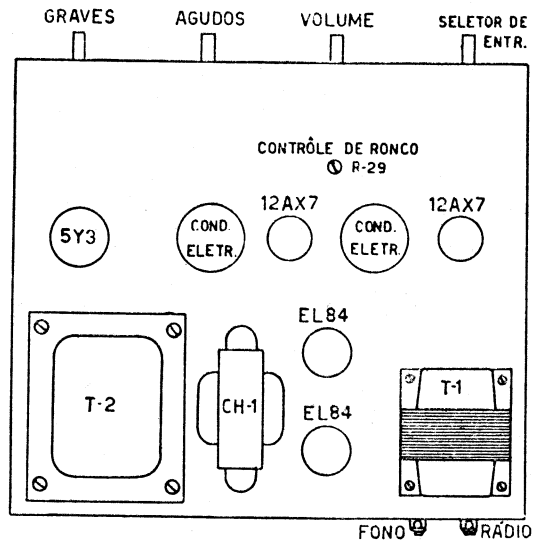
Distribuo dos componentes principais sbre o chassi.
